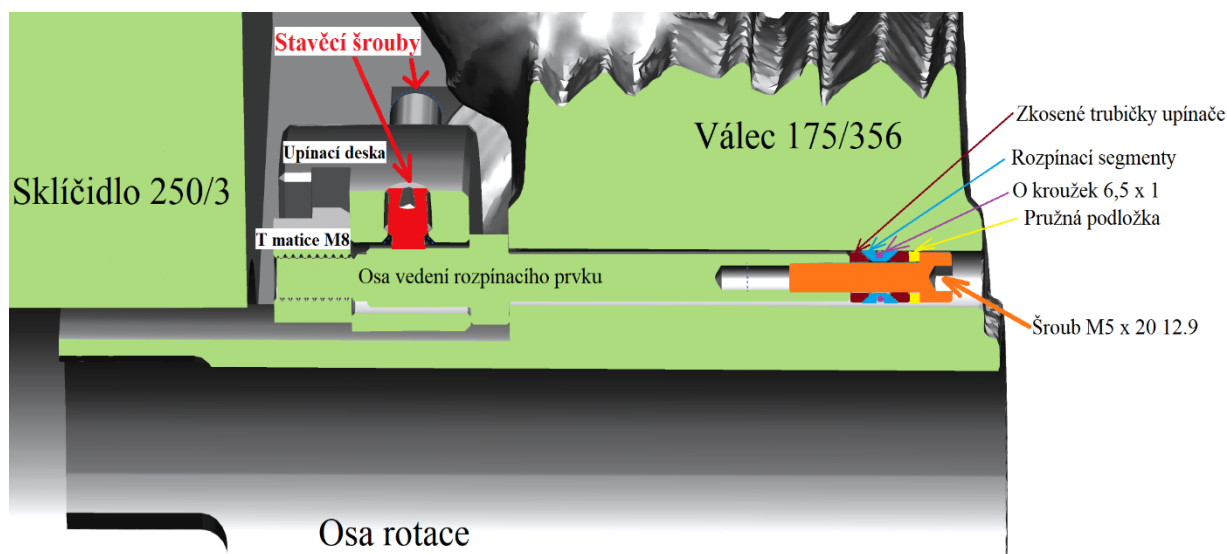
Přípravek pro upnutí hlavy válce s drážkou a spojovacím materiálem (modře označeným)
